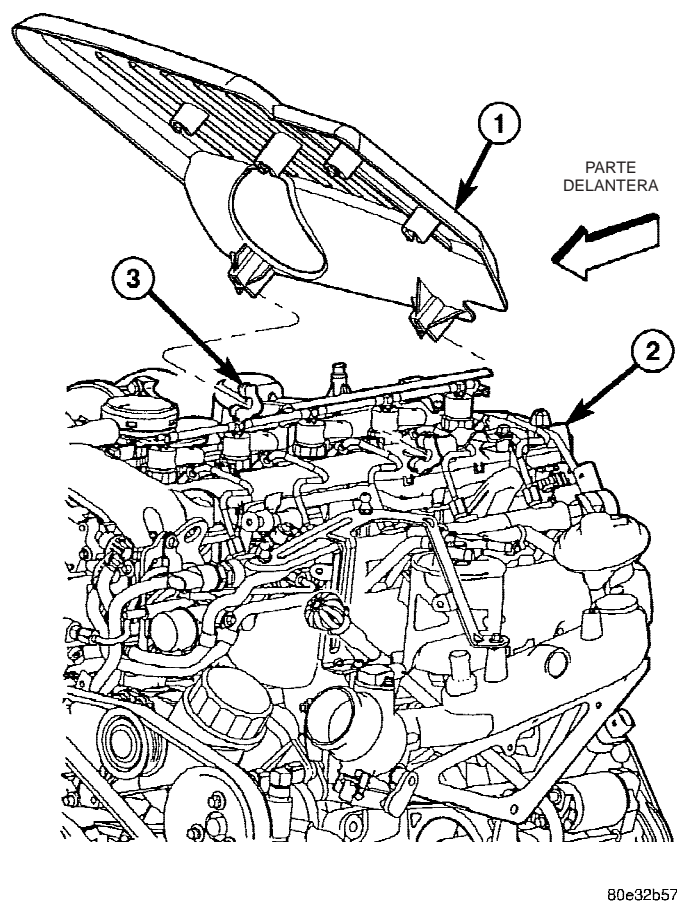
SOPORTES TRASEROS DE LA TAPA DEL MOTOR
